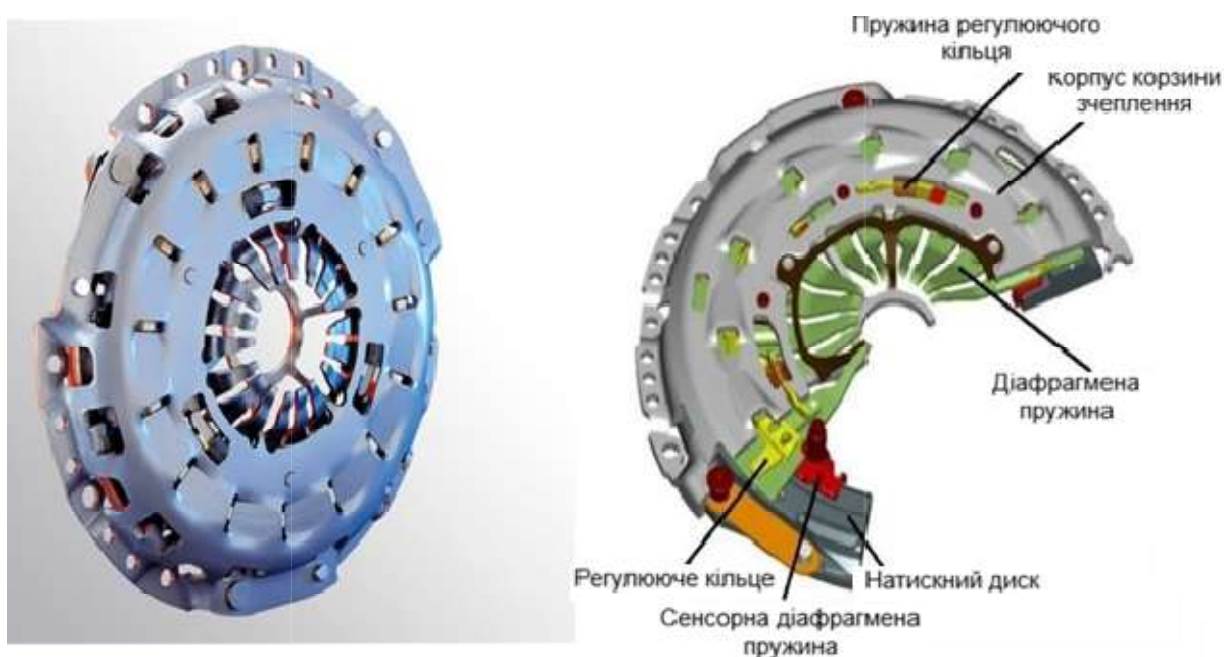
Загальний вигляд та елементи конструкції саморегулюючого зчеплення SAC
